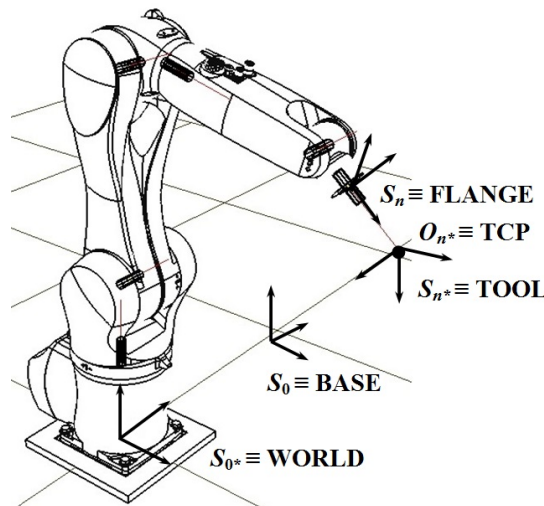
Системы координат: BASE, WORLD, FLANGE и TOOL
